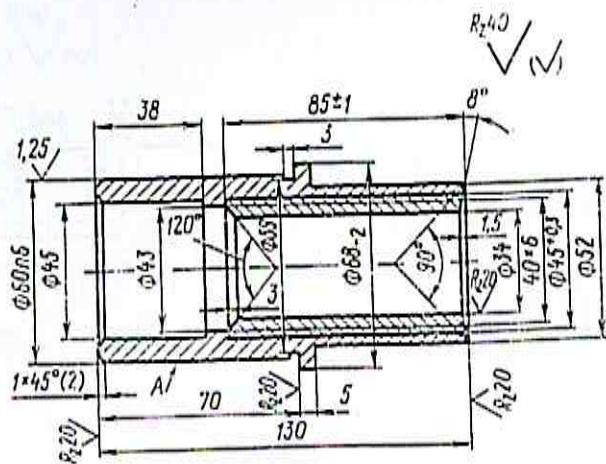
Гайка биметаллическая. Деталь 6М82.6.21А
